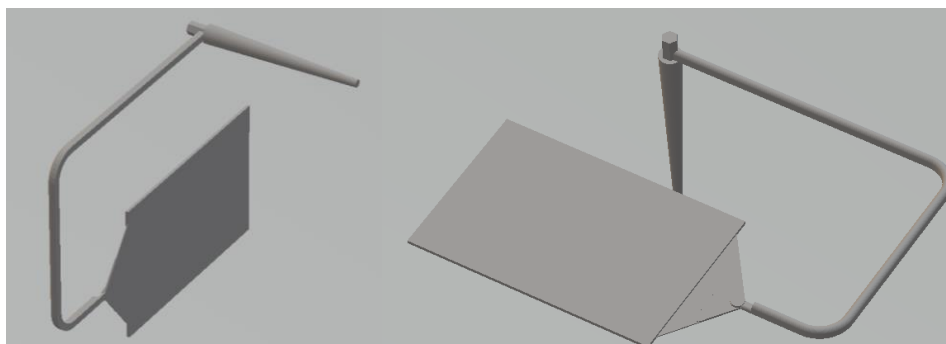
Vues 3D du moule plaque 2mm et du canal d'injection.
